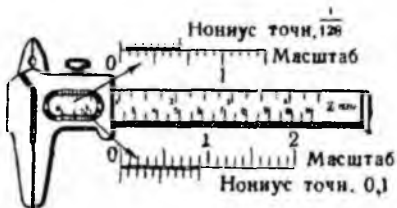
Нулевая установка штангенциркуля и нониуса.
